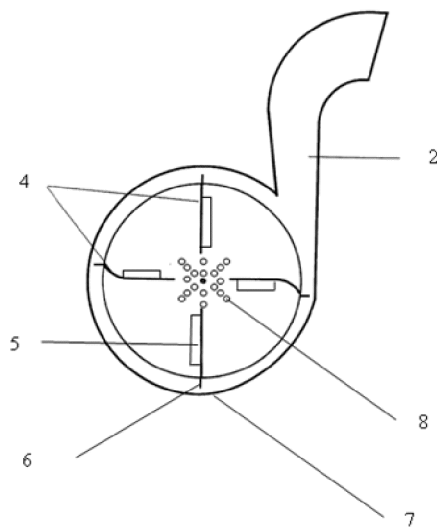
Общий вид рубительного диска и кожуха с отверстиями
